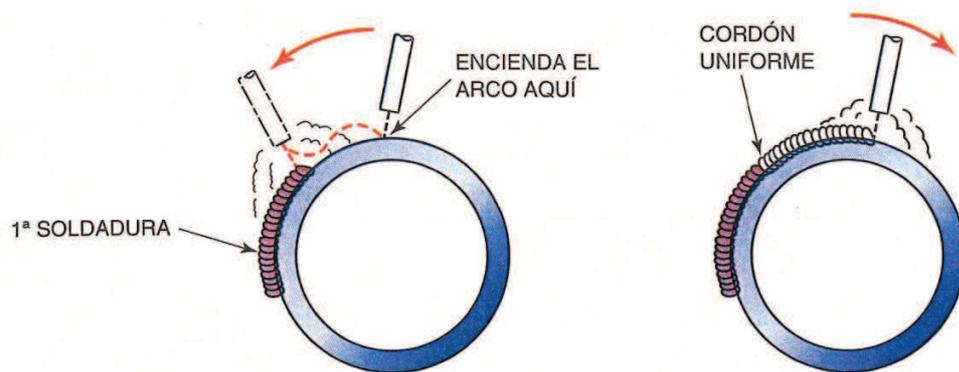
ÁREA DE SOLDADURA EN UN TUBO EN POSICIÓN HORIZONTAL
